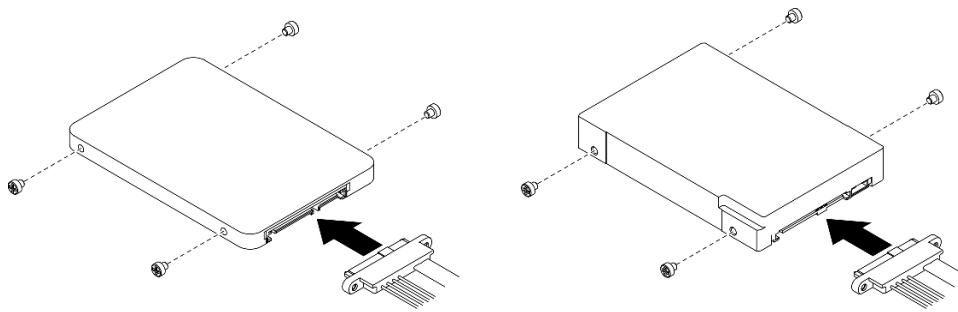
Installieren der Schrauben und Anschließen der Laufwerk Kabel
